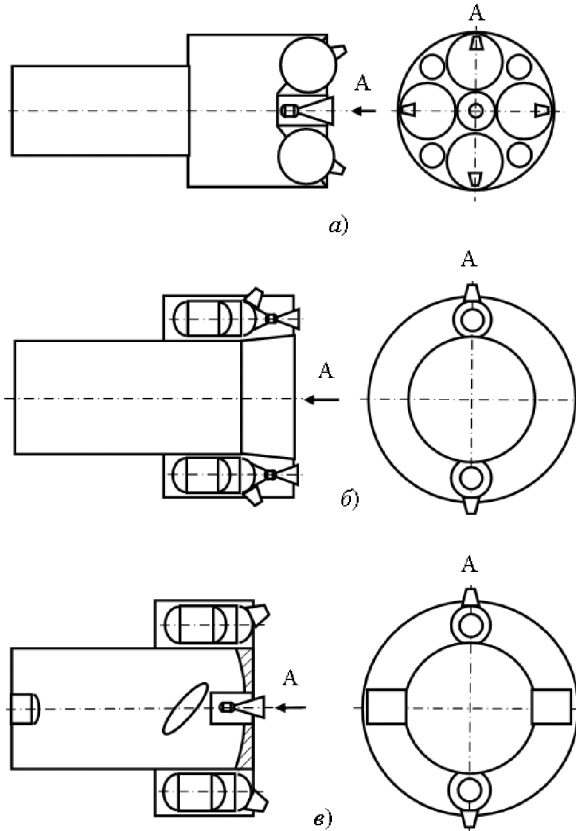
Схемы установки комплексной установки на космический аппарат
